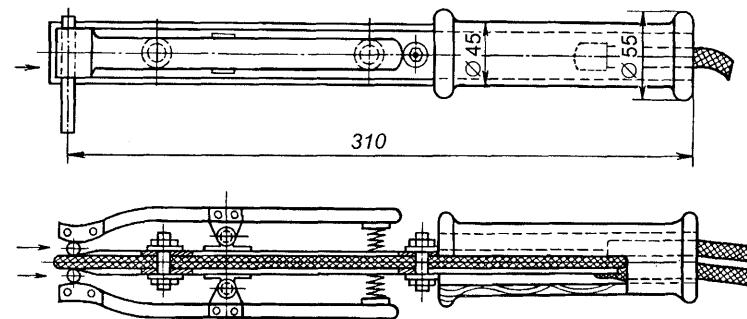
Электрододержатель для трехфазной сварки двумя параллельными электродами
